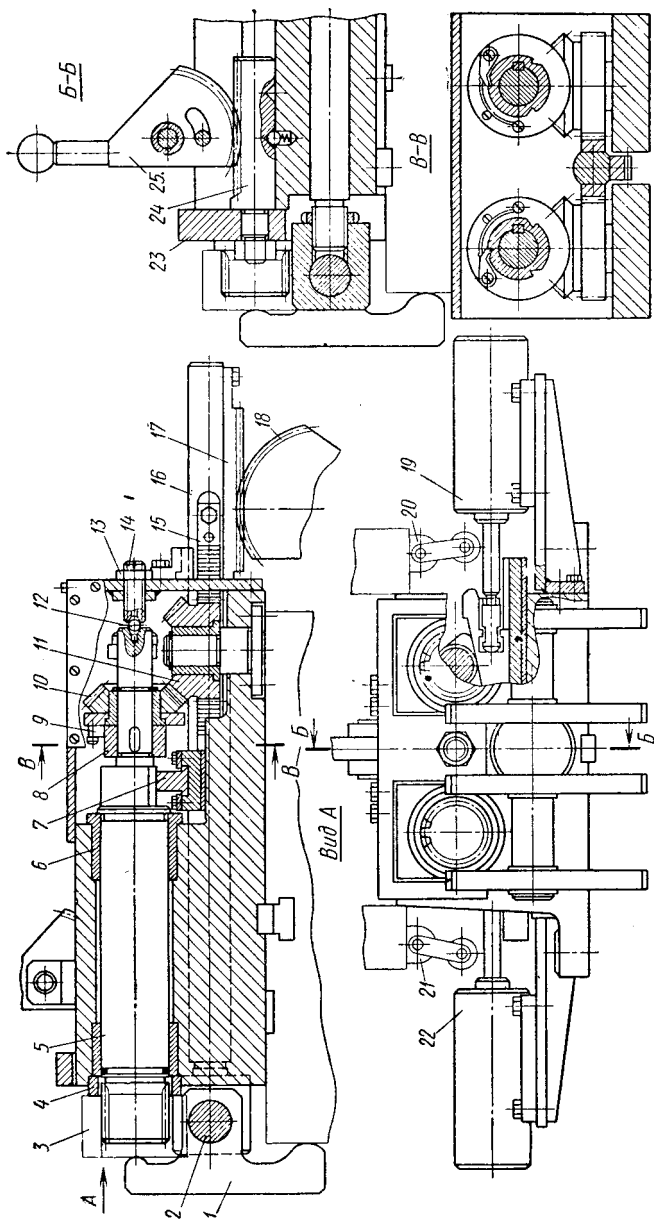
Многоместное приспособление для обработки полушаров на вертикально-протяжных станках с механизацией поворота заготовок
